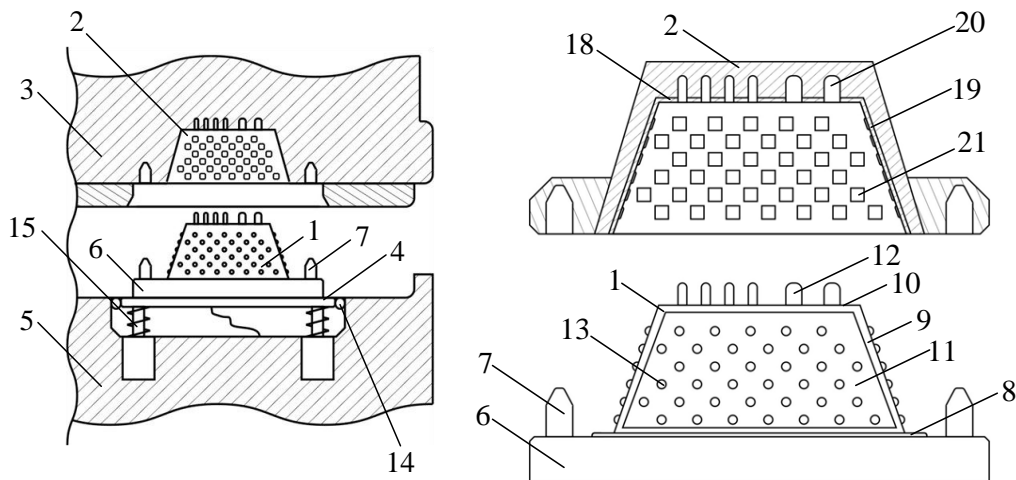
Схематичный вид на конструкцию УР: 1 – вилка; 2 – розетка; 3 – пусковой контейнер; 4 – подвижная платформа; 5 – ВПУ; 6 – основание; 7 – конусные штыри; 8 – уплотнительная прокладка; 9 – пирамидальный каркас; 10, 11 – съемные контактные поверхности; 12 – штыри; 13 – шарообразные контакты; 14 – резиновый валик; 15 – пружинный амортизатор
